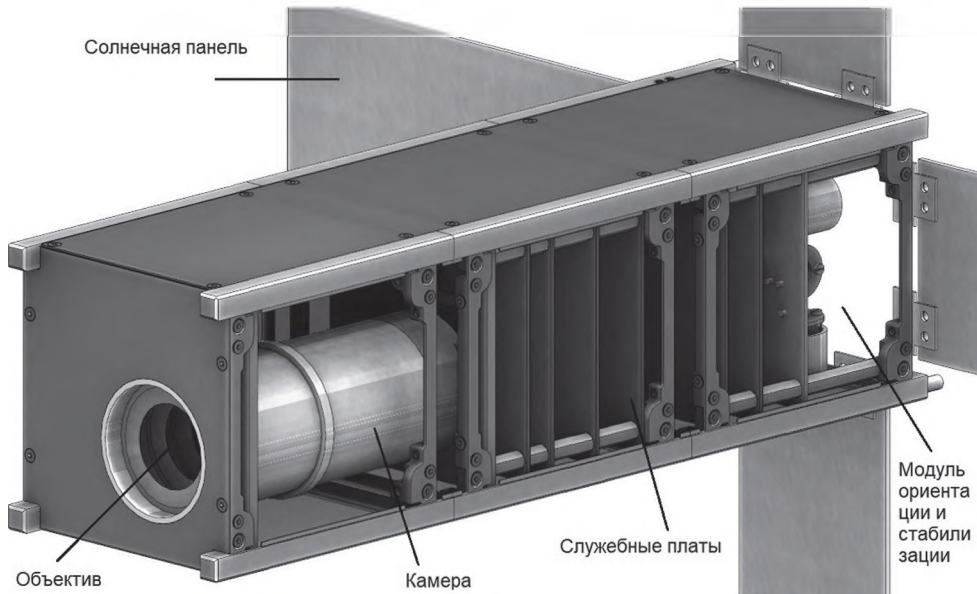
Предварительная компоновка оптической камеры на кубсате 3U
